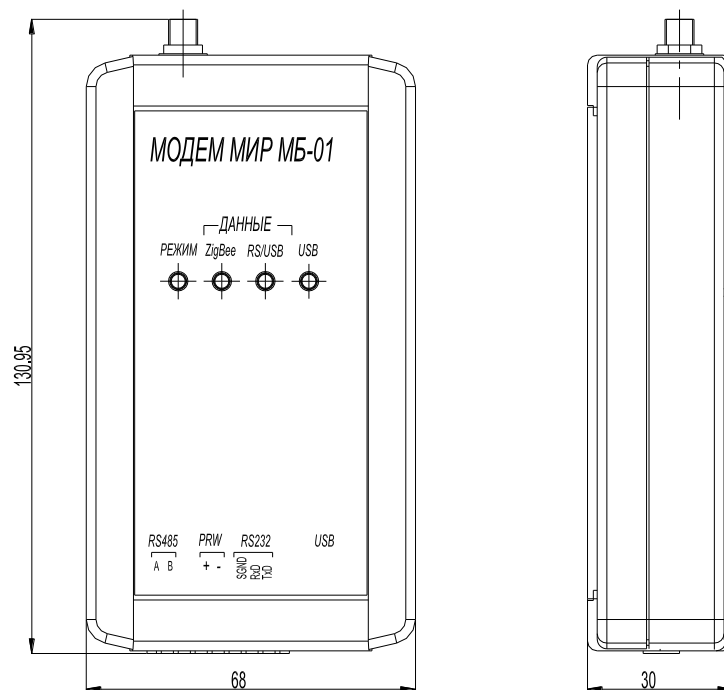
Внешний вид и габаритные размеры модема МБ-01.В
